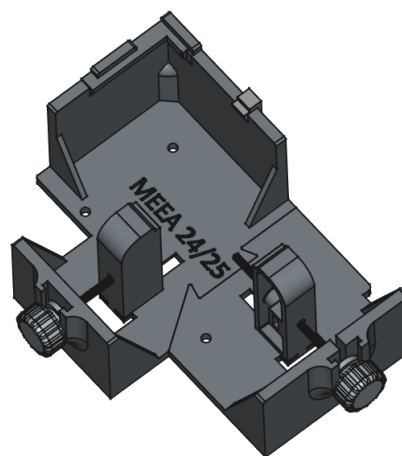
Base de posicionamento e fixação PCBAs em 3D
